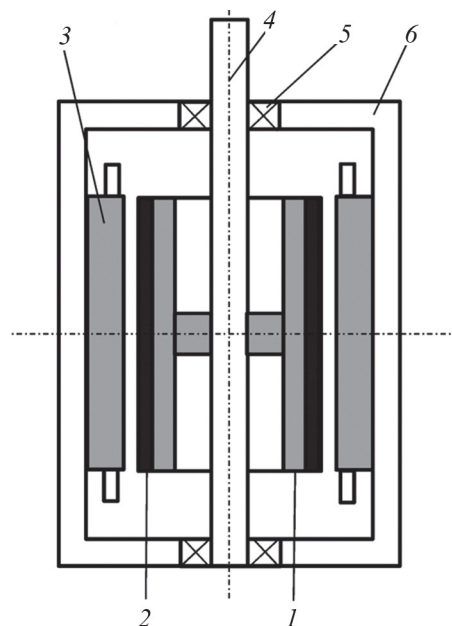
Компонка быстроходного генератора ротором в виде магнитного колеса:
